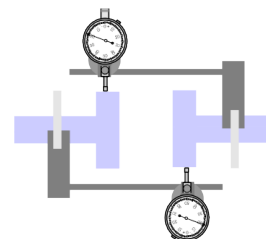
Método con Indicadores de Carátula en posición Reversed RIM. Cortesía Fixturlaser
